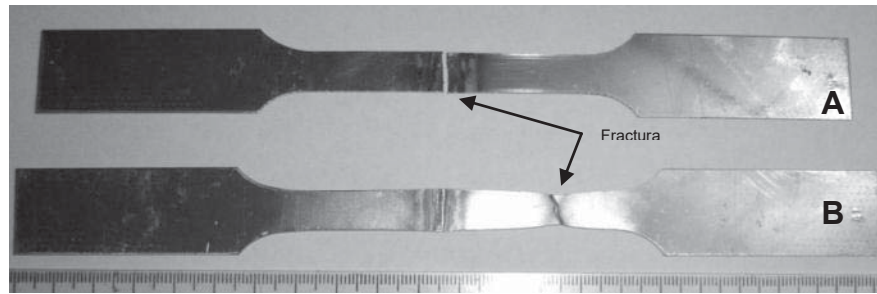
Localización de las fracturas: A) En el metal de soldadura y B) En el metal base.
